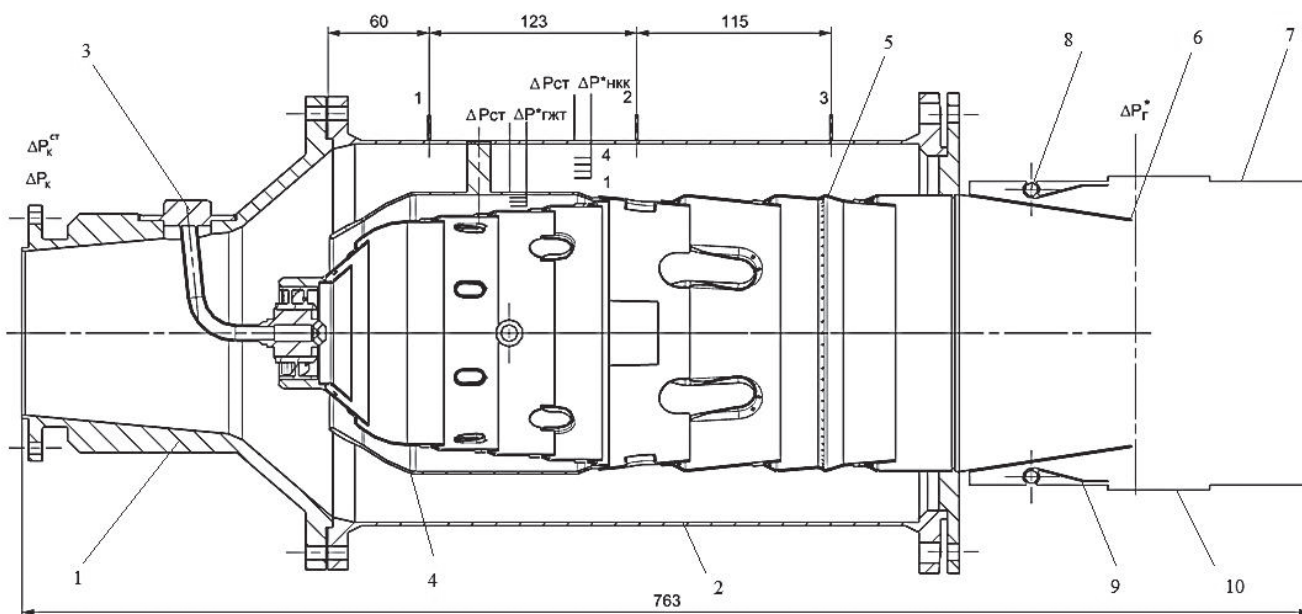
Конструктивная схема модели камеры сгорания: 1 — диффузор; 2 — корпус камеры сгорания; 3 — двух-контурная топливная форсунка; 4 — воздухозаборник; 5 — жаровая труба; 6 — газосборник; 7 — проставка; 8 — трубка подвода охлаждающего воздуха; 9 — дефлектор; 10 — окно для установки датчиков системы измерения и кварцевых стекол
